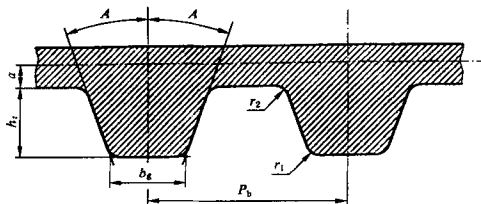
加工 ZA 和 ZB 型带轮齿条刀具
